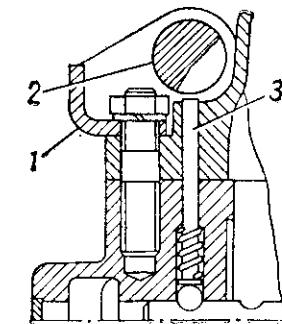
Установка валика блокировочного механизма (положение при выжатой педали сцепления):
